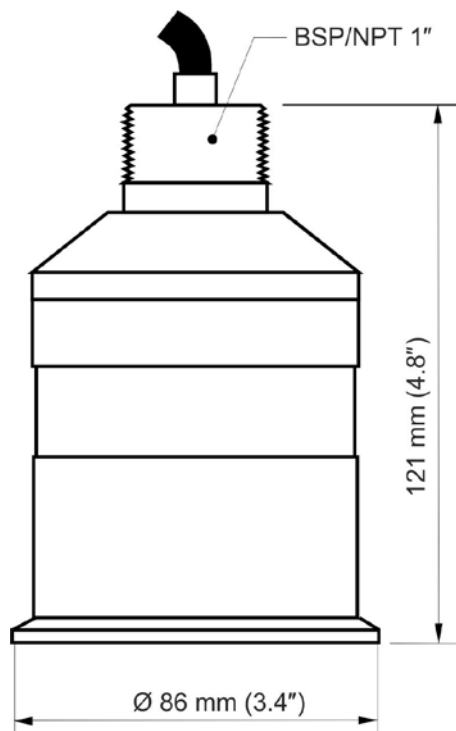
Abmessungen i-Sensor Typ 06m und Typ 10 mit Einbaugewinde kableseitig
